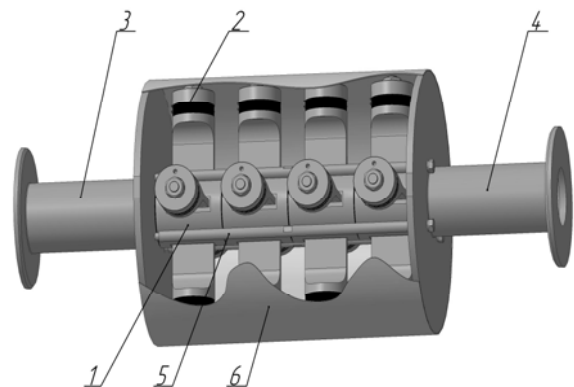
Устройство ультразвуковой кавитационной проточной обработки (1 – кольцевой ультразвуковой вибратор; 2 – ультразвуковой излучатель; 3 - входной патрубок; 4 – выходной патрубок; 5 – стягивающая шпилька; 6 – корпус)
